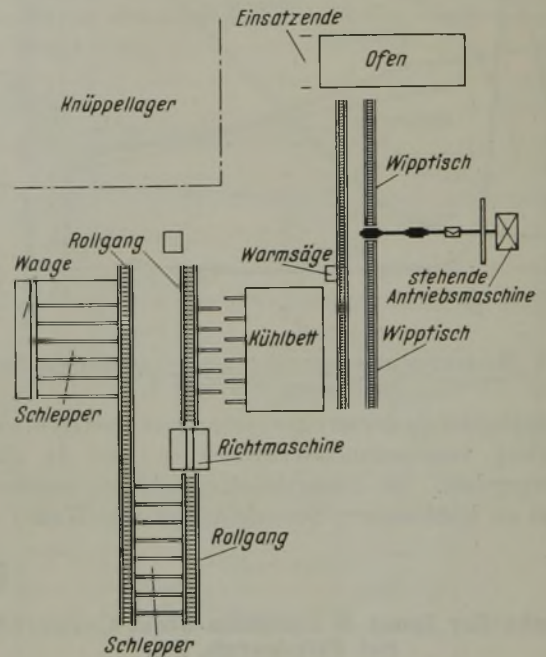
Lageplan der 610er Stabstahlstraße (Nr. 13).
